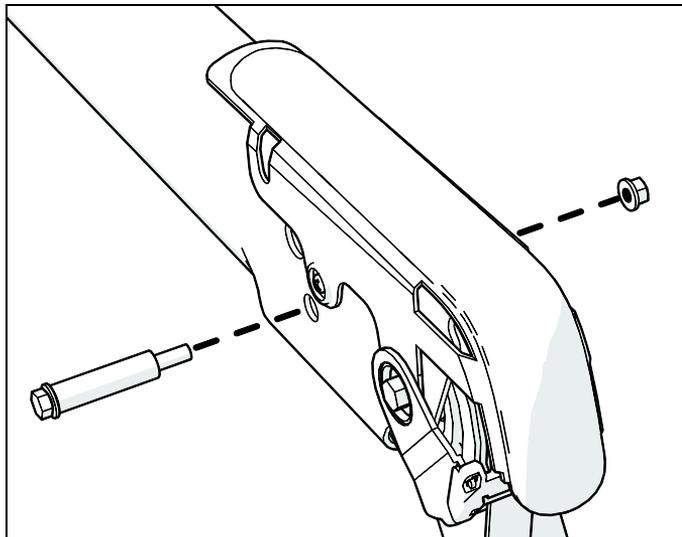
Fixação de parafuso e bucha para instalar suporte lateral
